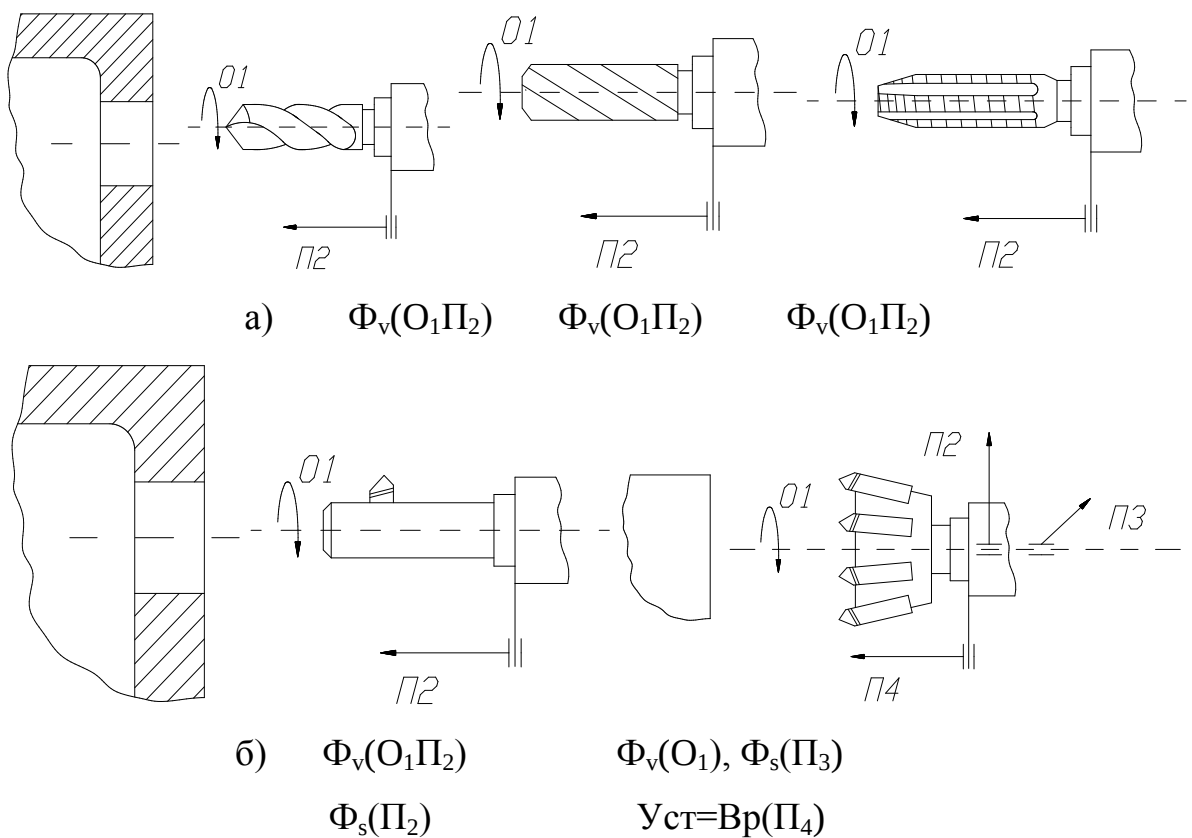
Схеми формоутворення поверхонь деталей
